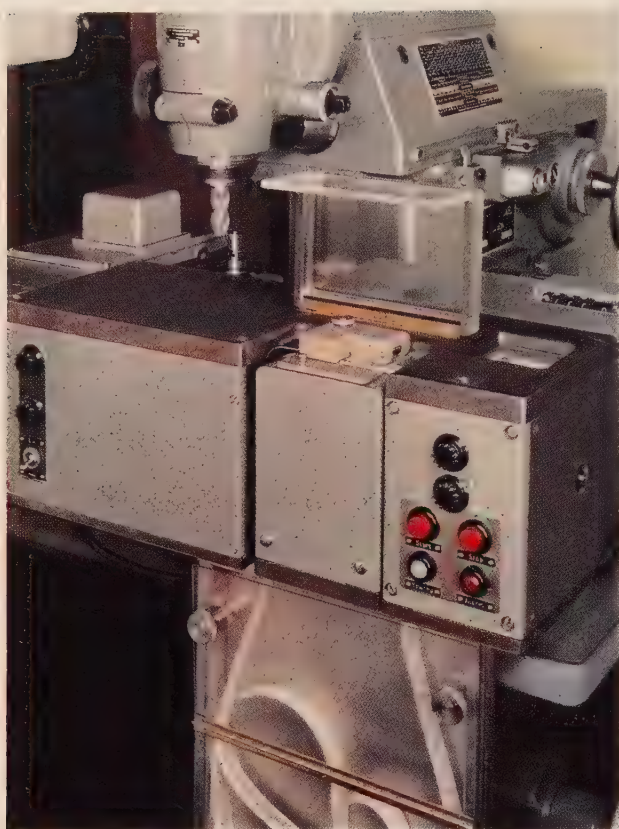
Lochstreifen-Abtaster zum Steuern einer Fräsmaschine
